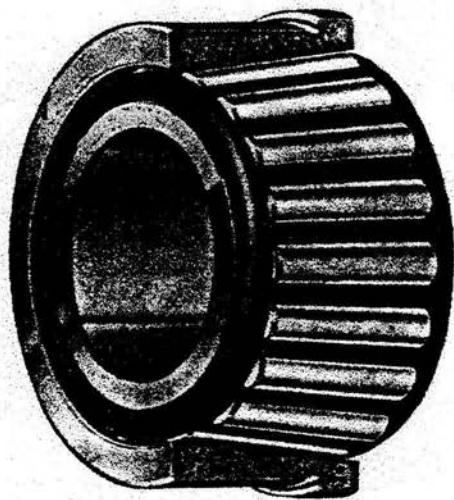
Rodamiento de una hilera de rodillos con pestaña en la pista exterior
